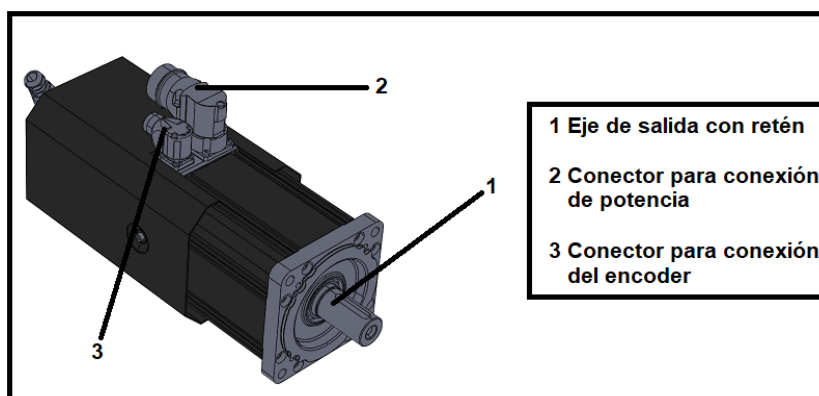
CAD del motor con el detalle de sus partes [23].
